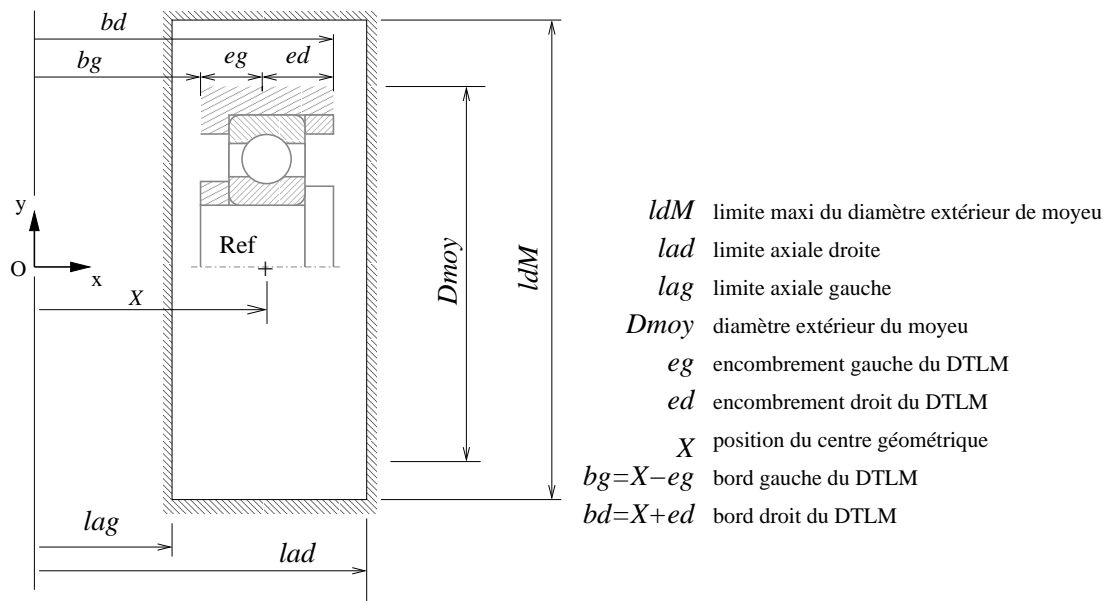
Contraintes d'encombrement sur un DTLM.
